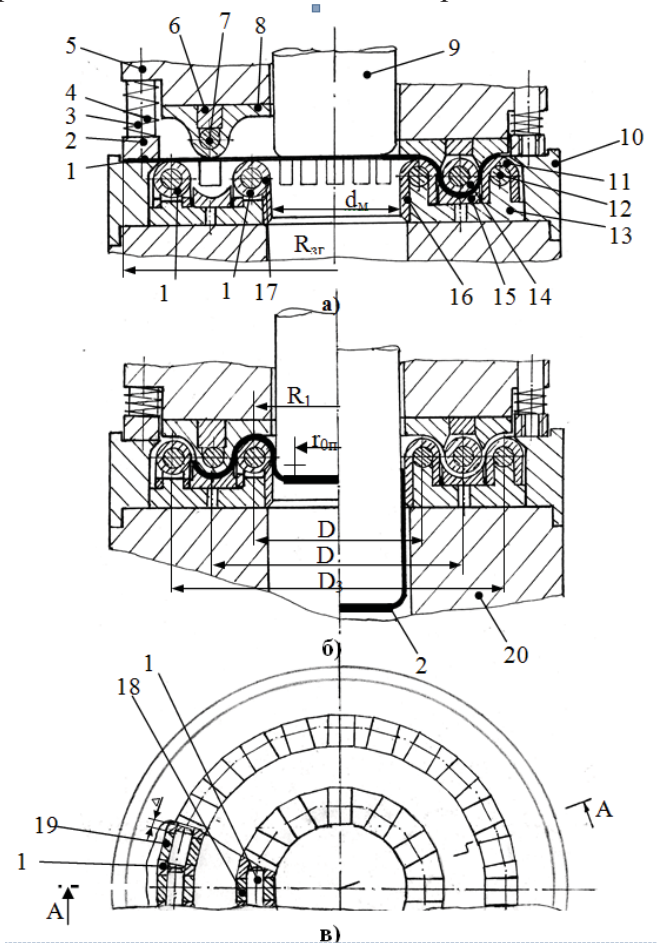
Продольный разрез штампа для глубокой вытяжки:
